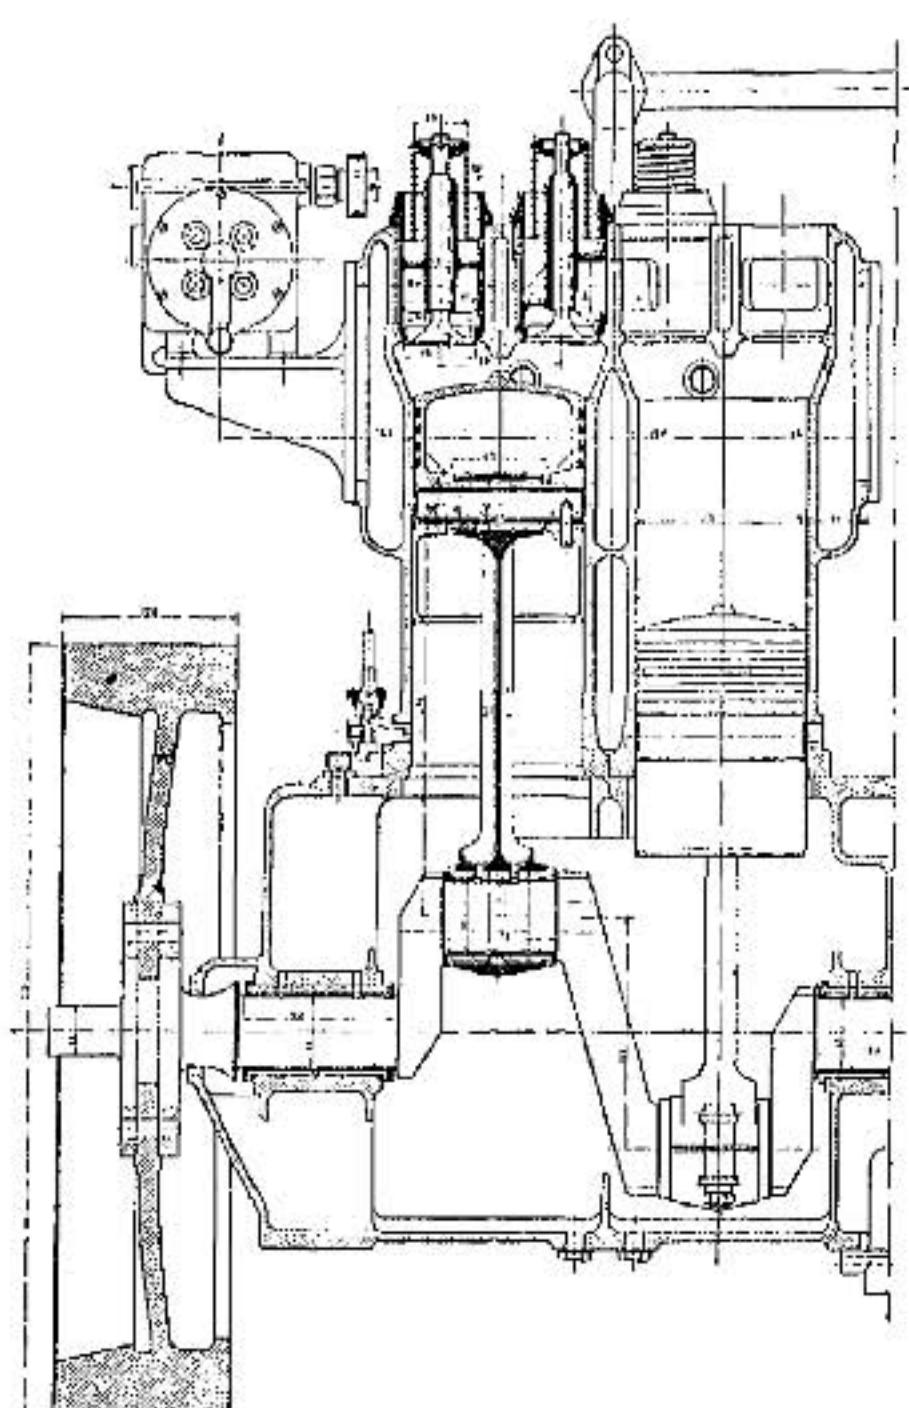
Клапана со смѣнными втулками двигателя Бюссингъ.
